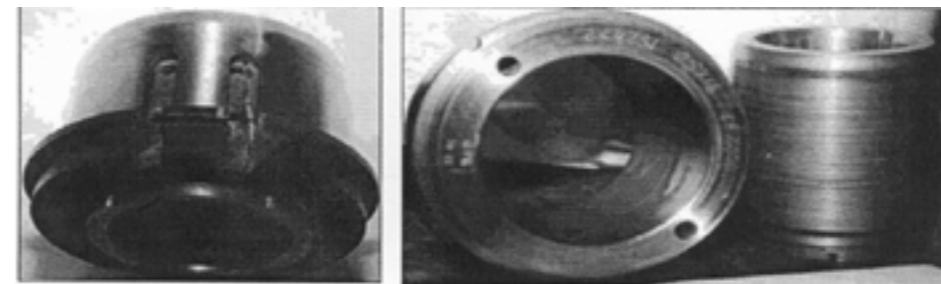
Фрезерованные пазы для гидростатического подвода конденсата
